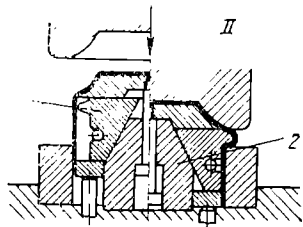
Формовочный штамп: положение: 1 — до формовки, 2 — после формовки
